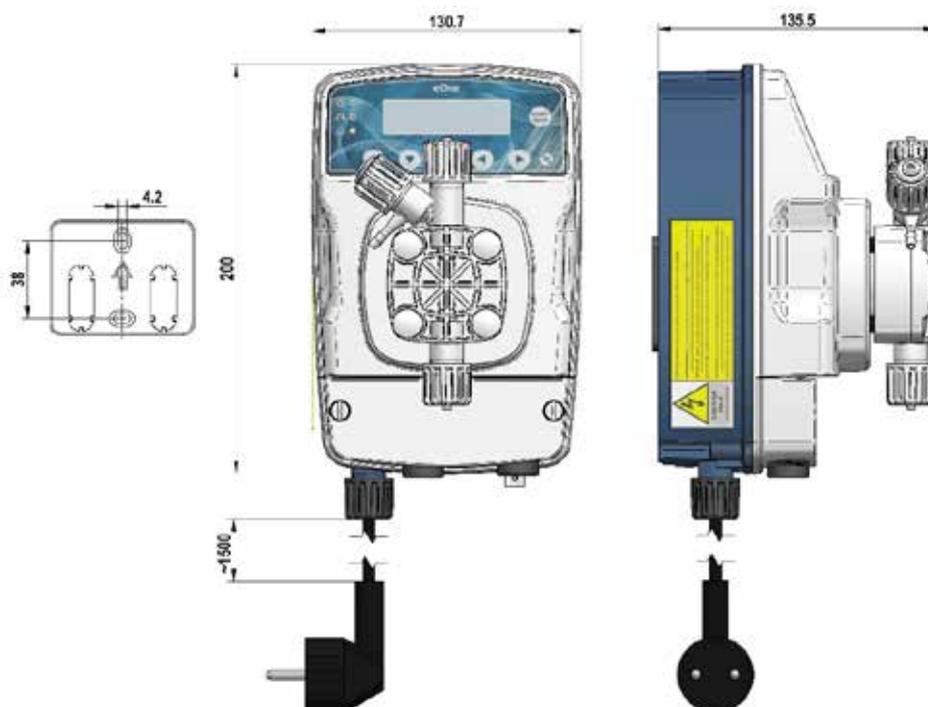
Bomba y placa para montaje en pared (dimensiones en mm.)
